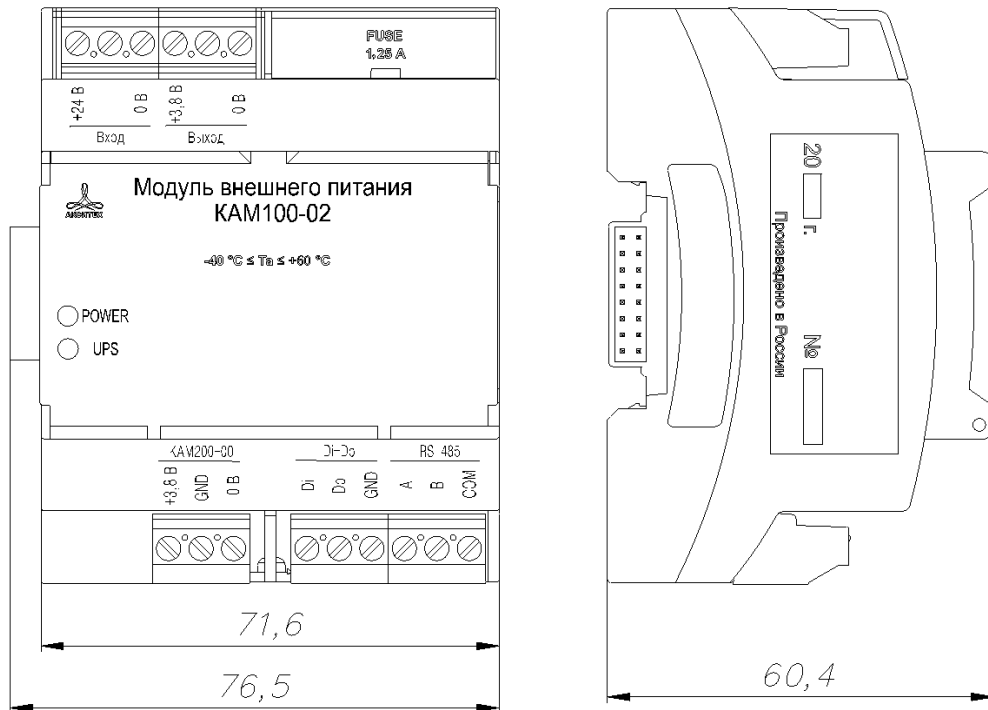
Внешний вид и габаритные размеры модуля бесперебойного питания KAM100-02
